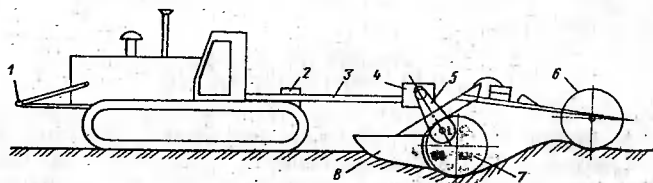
Машина для глубокого фрезерования закустаренных земель: 1 — ствол; 2 — установка ходоуменьшителя; 3 — вал карданный; 4 — редуктор конический; 5 — редуктор бортовой; 6 — опора задняя; 7 — фреза с редуктором; 8 — плита отбойная
